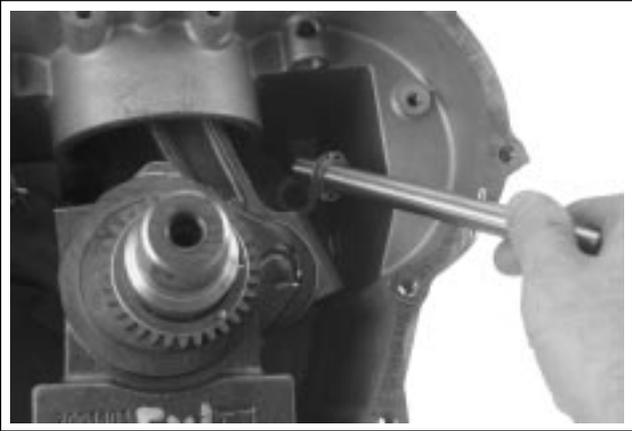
Dépose de l'arbre à cames du côté échappement et de la rondelle de butée fendue.
